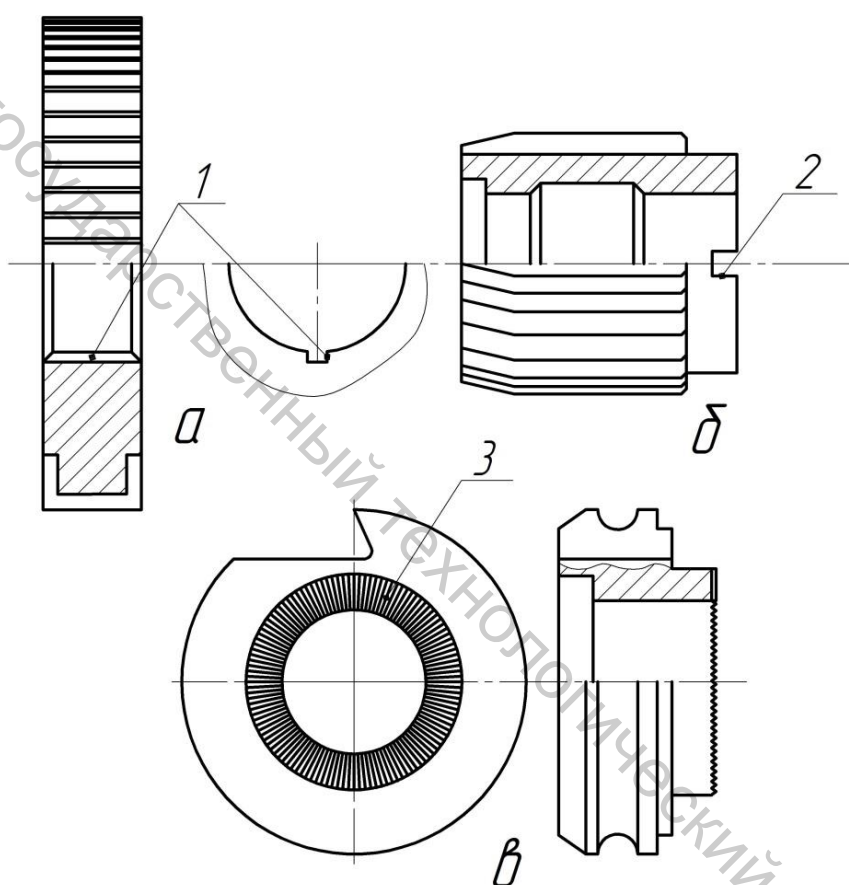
Виды внутренних баз металлорежущих инструментов:
